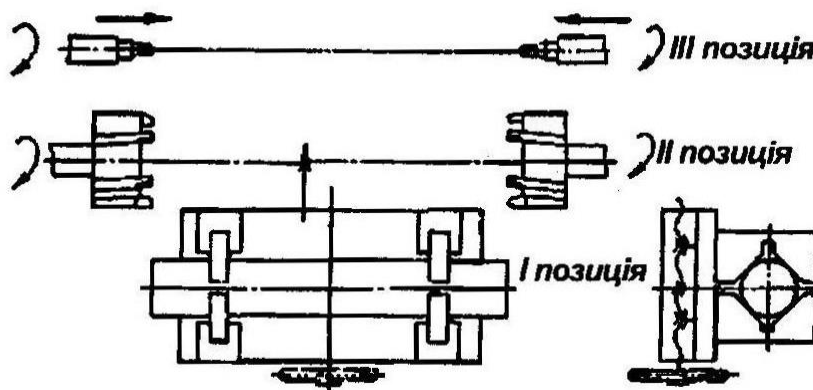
Принцип роботи фрезерно-центрувального верстата
